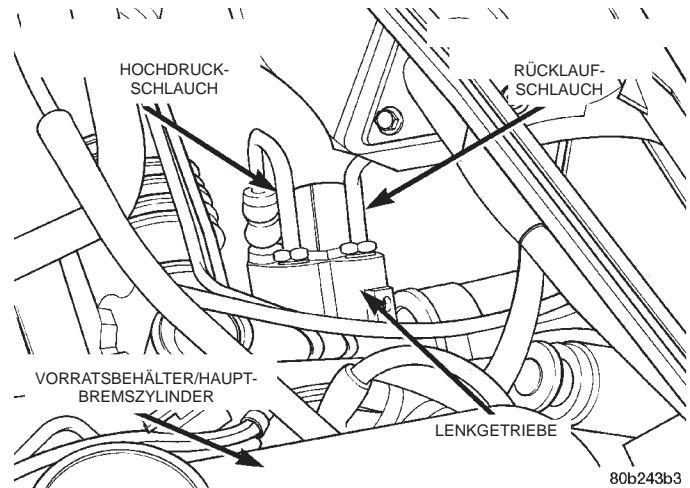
Anschlüsse der Ölschläuche am Lenkgetriebe
